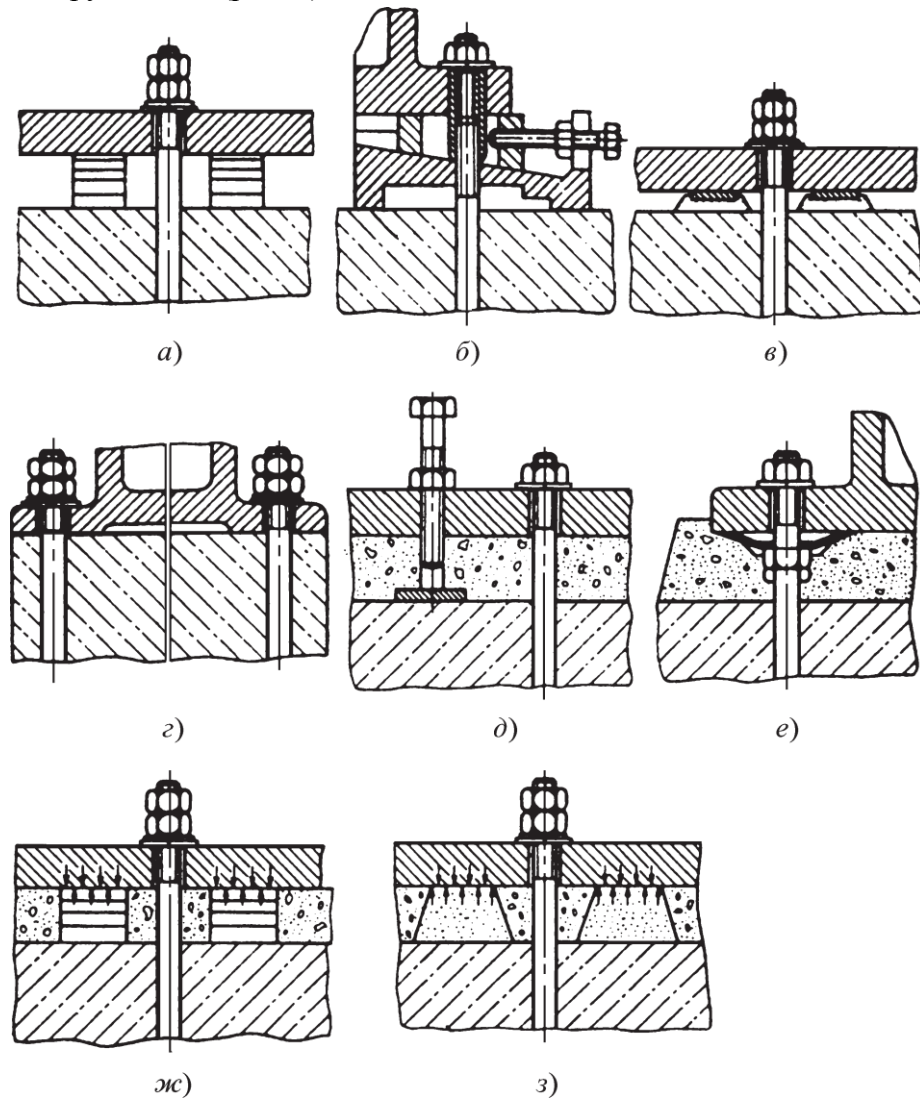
Основные конструкции стыка корпусная деталь—фундамент: с местным опиранием на пакеты подкладок (а), на опорные башмаки (б), на бетонные опоры (в) и непосредственно на фундамент (г); со сплошным опиранием на бетонную подливку с временной установкой при выверке на отжимных винтах (д) и на установочных гайках (е); со смешанным опиранием на подливку и опорные элементы (ж и з)
